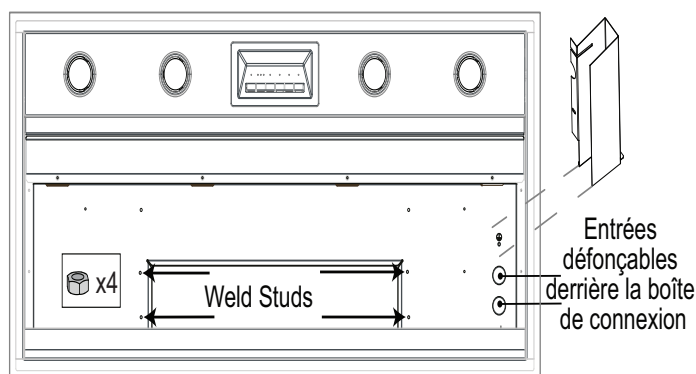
Emplacement des tiges soudées et de la boîte de connexion
